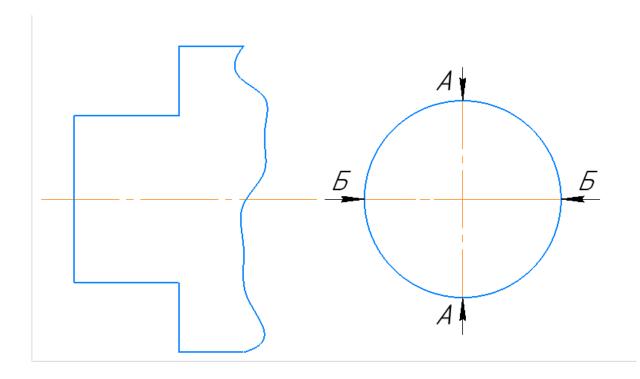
Эскиз вала Рисунок 2 — Схема измерения
